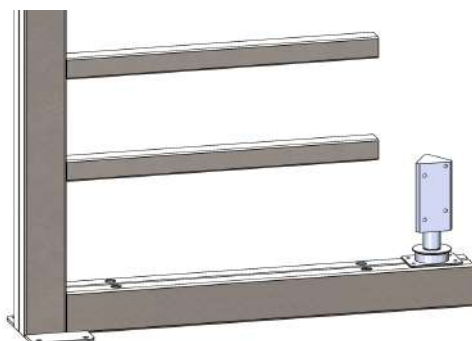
Установленная призма верхнего подшипникового узла
